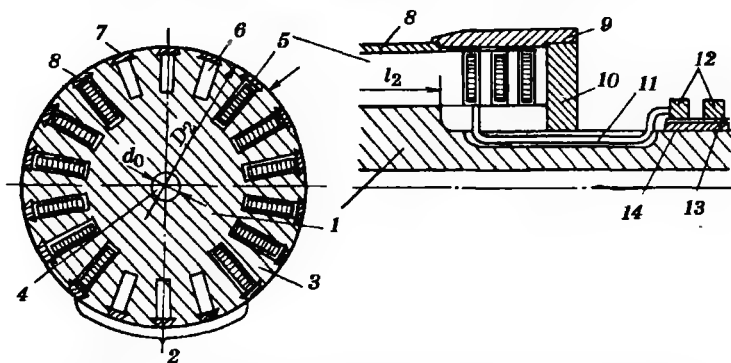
Поперечный и продольный разрезы неявнополюсного ротора
